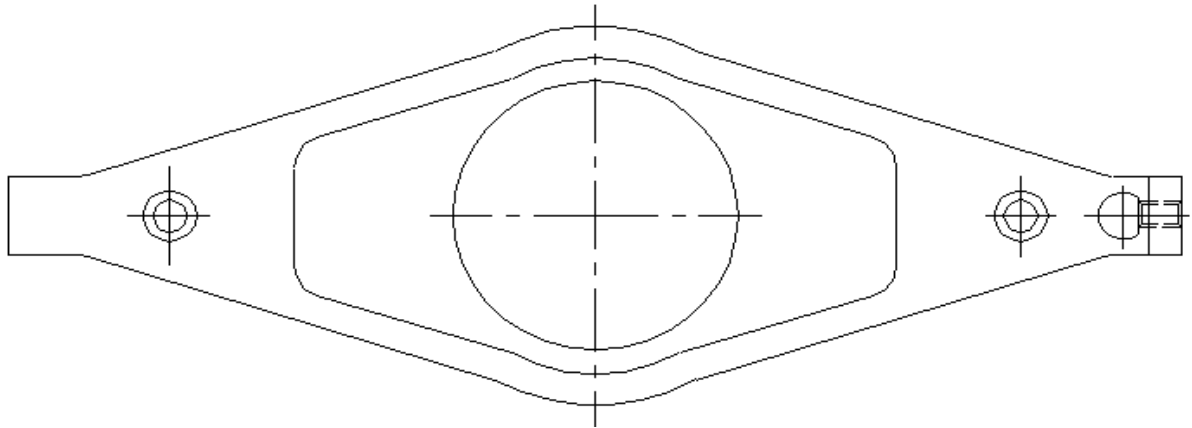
PLATO PORTA-HERRAMIENTAS
